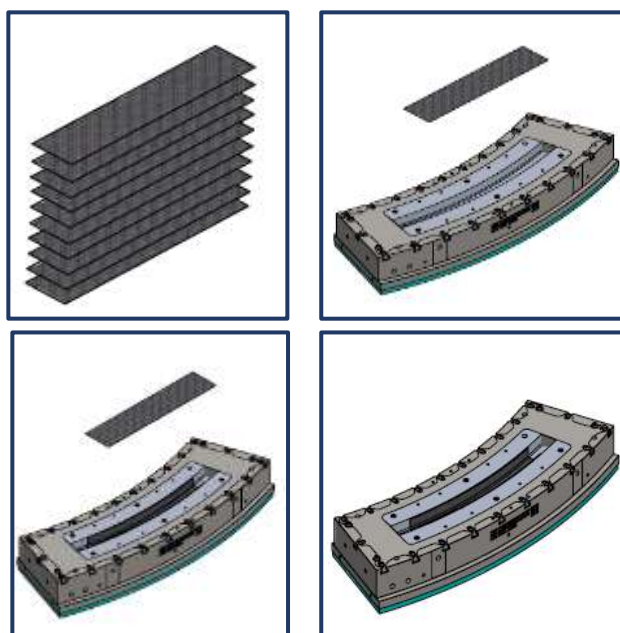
Montaje de la preforma en el molde cóncavo.
